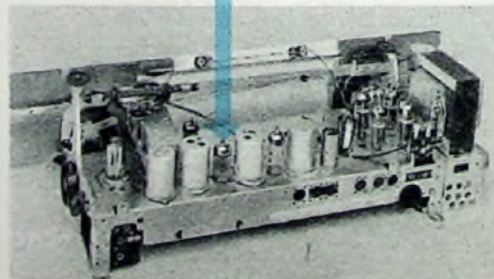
b. Chassisansicht der Musiktube „Ballerina Konzert Stereo“
